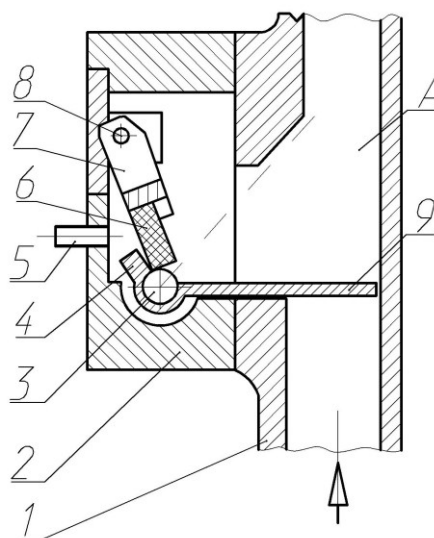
Клапан перепускной 1 — коллектор; 2 — корпус клапана; 3 — ось заслонки; 4 — упор; 5 — штуцер с отверстием; 6 — клапан; 7 — рычаг; 8 — ось рычага; 9 — заслонка
